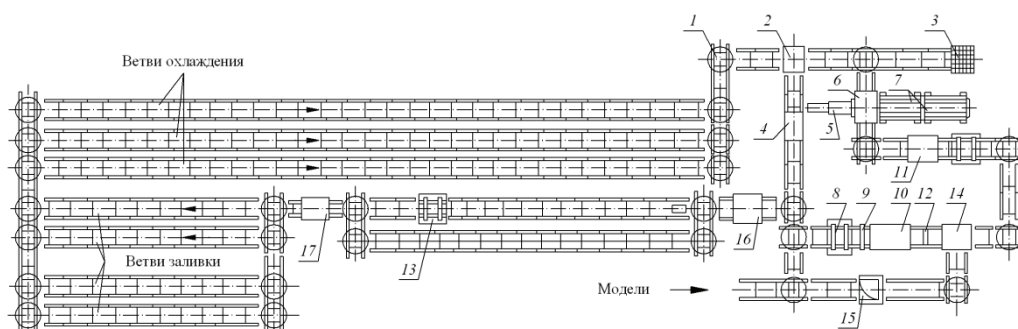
Планировка линии модели Л653С: 1 – поворотный стол; 2 – механизм съема форм с поддона; 3 – выбивная решетка бракованных отливок; 4 – механизм очистки поддонов; 5 – сталкиватель кома; 6 – выбивной пресс; 7 – выбивная решетка; 8 – механизм вытяжки; 9 – механизм срезания излишков смеси; 10 – механизм встряхивания и прессования; 11 – механизм очистки и распаровки опок; 12 – дозатор формовочной смеси; 13 – кантователь опок; 14 – механизм сборки опок с моделью; 15 – дозатор облицовочной смеси; 16 – механизм установки полуформ на поддоны; 17 – механизм сборки форм
